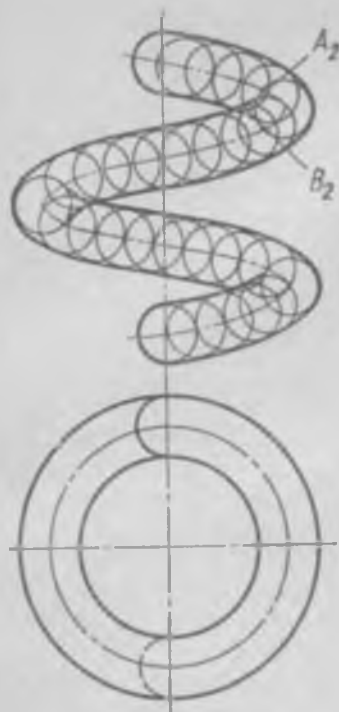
Пример винтового цилиндра — змеевик, пружина
